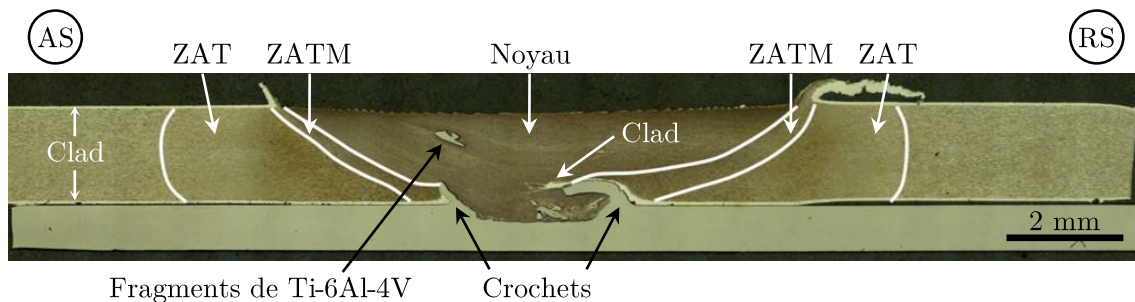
Coupe transversale d'une soudure prise au microscope optique.
